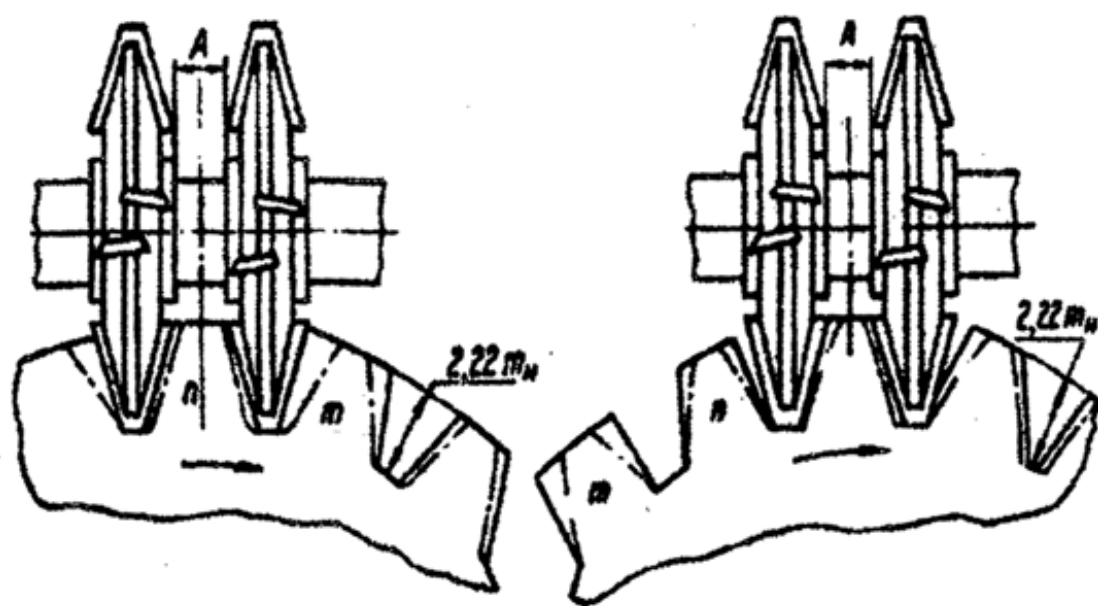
Схема прорезания дисковыми фрезами зубчатых колес с числом зубьев менее 60:
